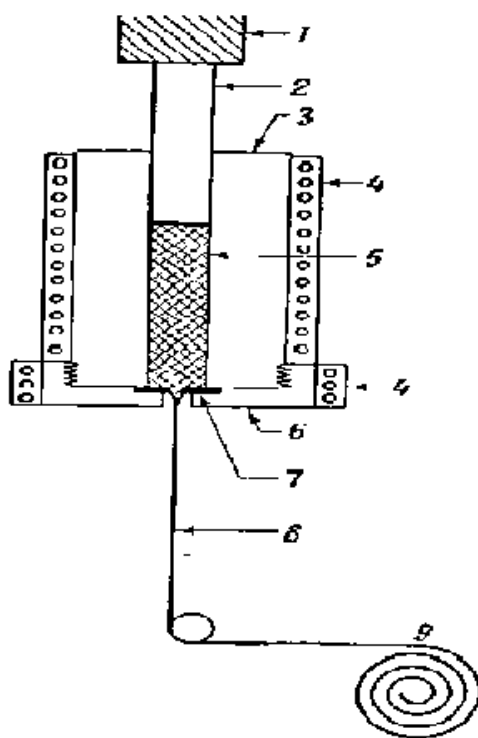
Аппарат для прядения из расплава: 1 – гидравлический пресс; 2 – поршень; 3 – цилиндр; 4 – нагревательное устройство; 5 – расплавленный полимер; 6 – устройство для поддержания фильеры; 7 – фильера; 8 – нить; 9 – бобина
